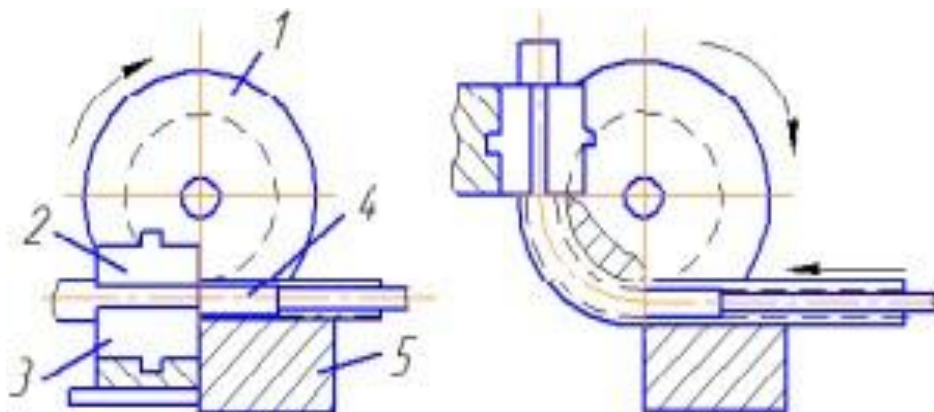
Конструктивна схема інструмента для згинання заготовки труби намотуванням
